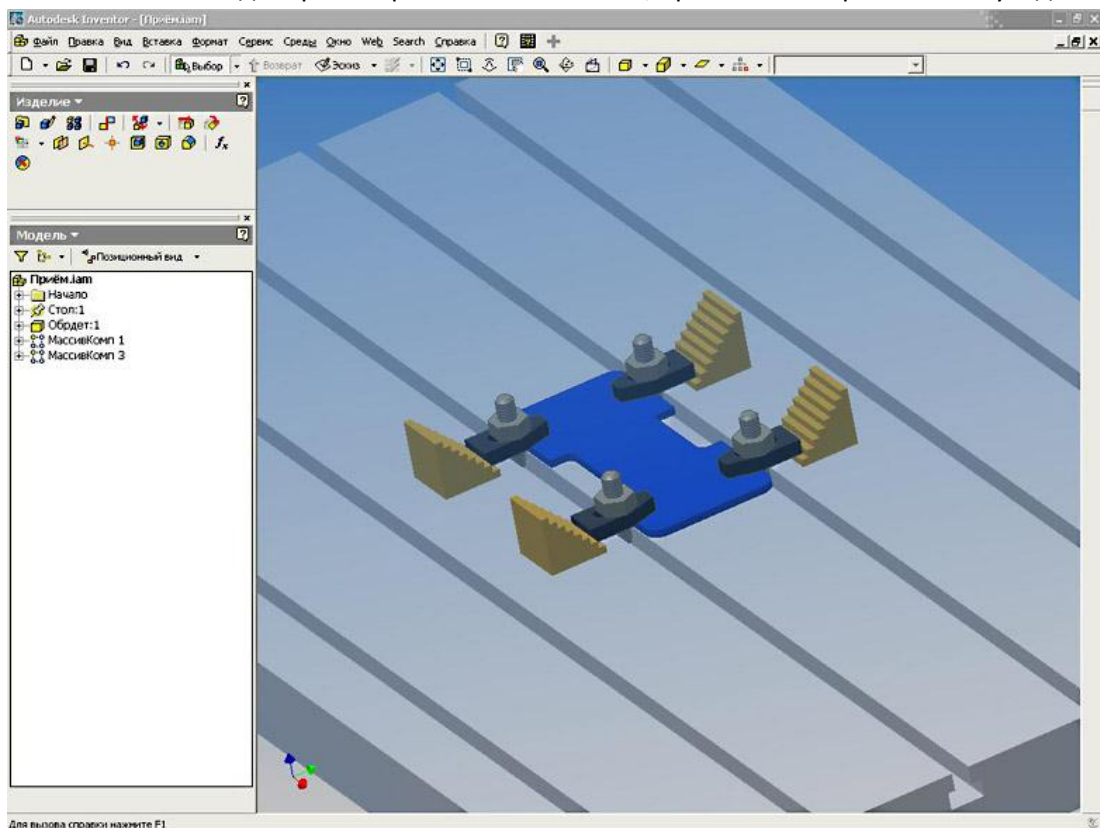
Моделируем рабочий стол станка, прижимы и обрабатываемую деталь
